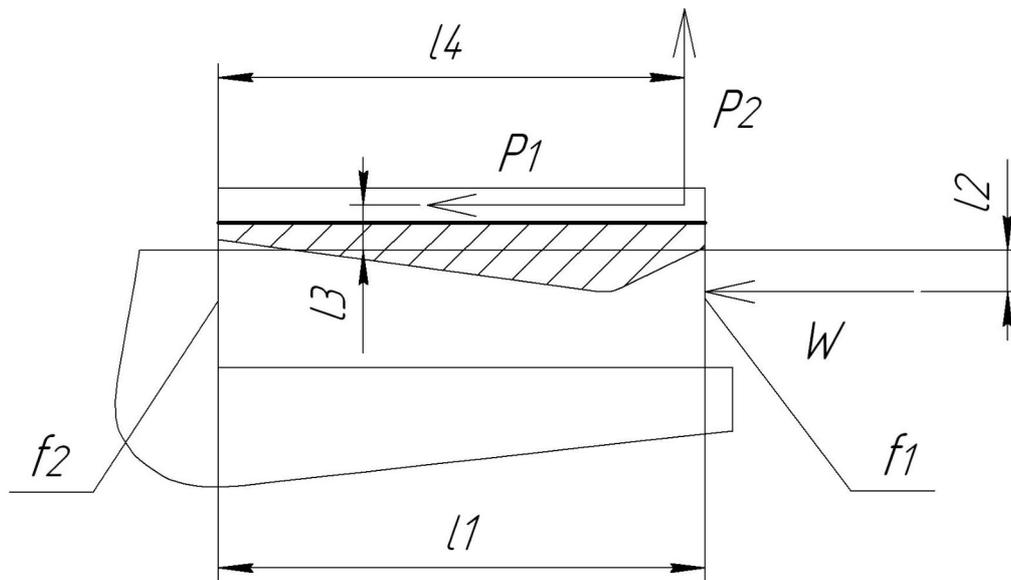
Схема сил, действующих на заготовку при фрезеровании
